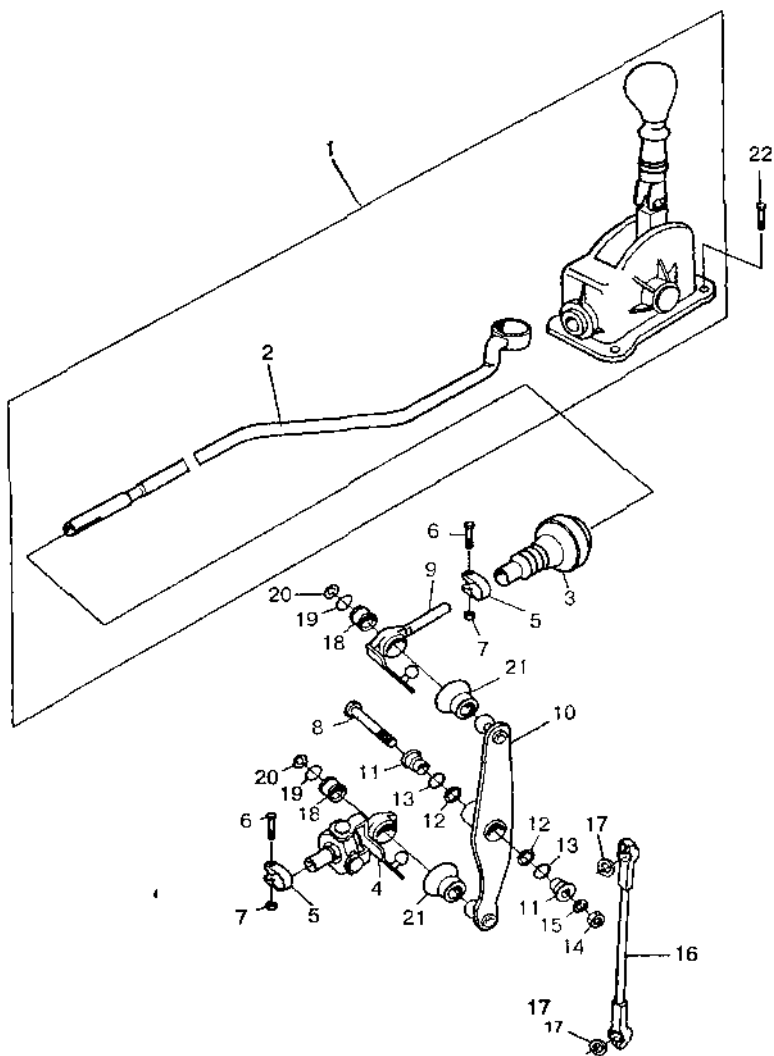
Привод управления механизмом переключения передач: 1 - привод переключения передач в сборе; 2 - вал механизма переключения передач; 3 - чехол трубы в сборе; 4 - шарнир карданный в сборе; 5 - хомут стяжной вилки шарнира; 6, 22 - болты; 7, 14 - гайки; 8 - ось рычага; 9 - хвостовик шарнира в сборе; 10 - рычаг в сборе; 11 - втулка ступицы рычага; 12 - кольцо демпфирующее ступицы; 13 - кольцо уплотнительное ступицы; 15 - шайба; 16 - тяга выбора в сборе; 17 - уплотнитель шарнира тяги выбора; 18 - вкладыш шарнира; 19 - кольцо вкладыша уплотнительное; 20 - заглушка шарнира; 21 - грязеотражатель шарнира; 22 - болт специальный.
